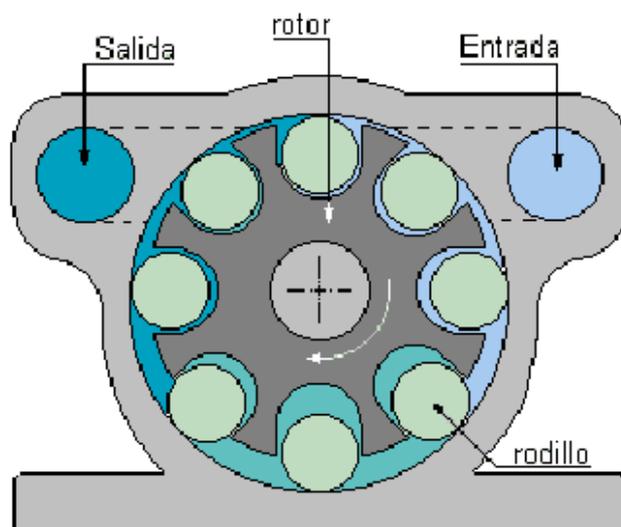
Vista en corte de una bomba de rodillos. Fuente Onorato - Tesouro
